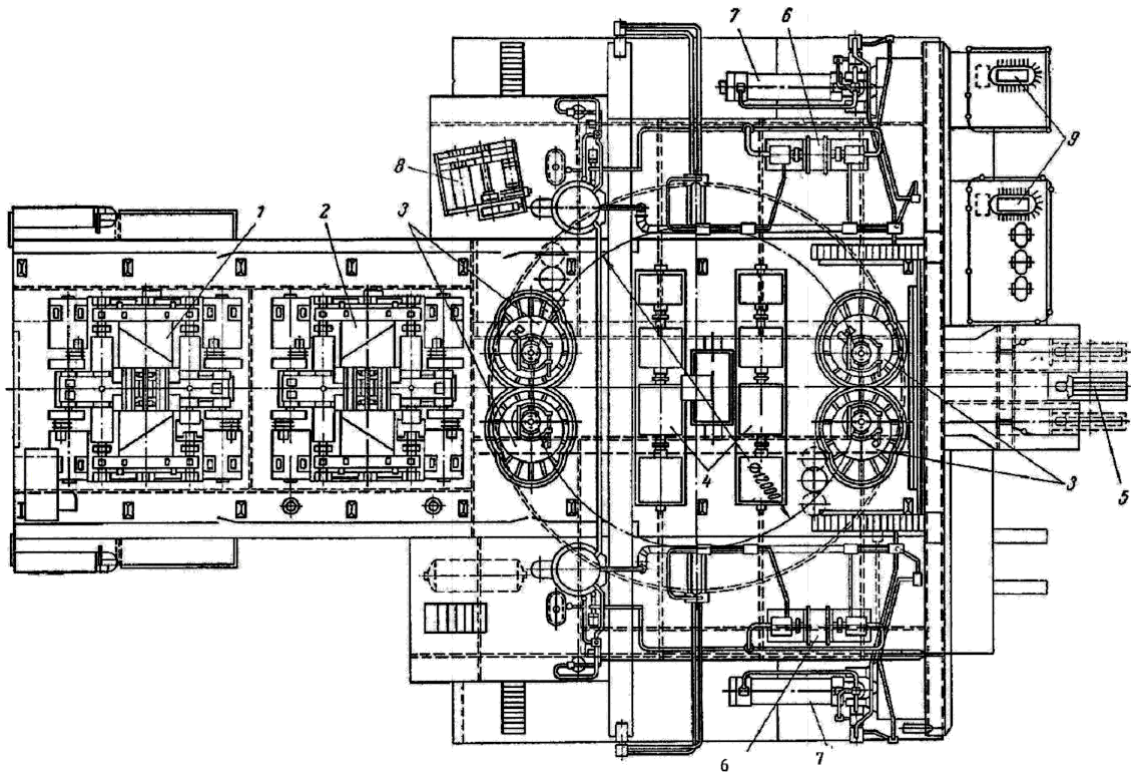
Розташування механізмів на першому ярусі поворотної платформи екскаватора ЕШ-25/100
